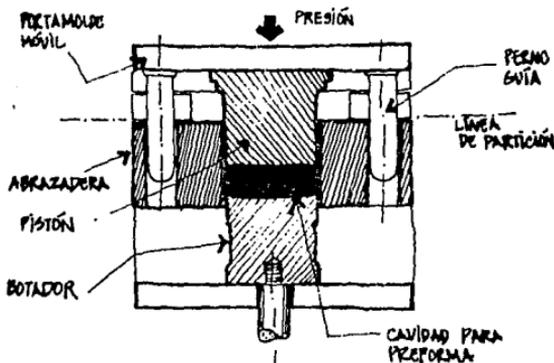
Corte esquemático de un sencillo molde de "pastillaje" en frío. Doble acción.
